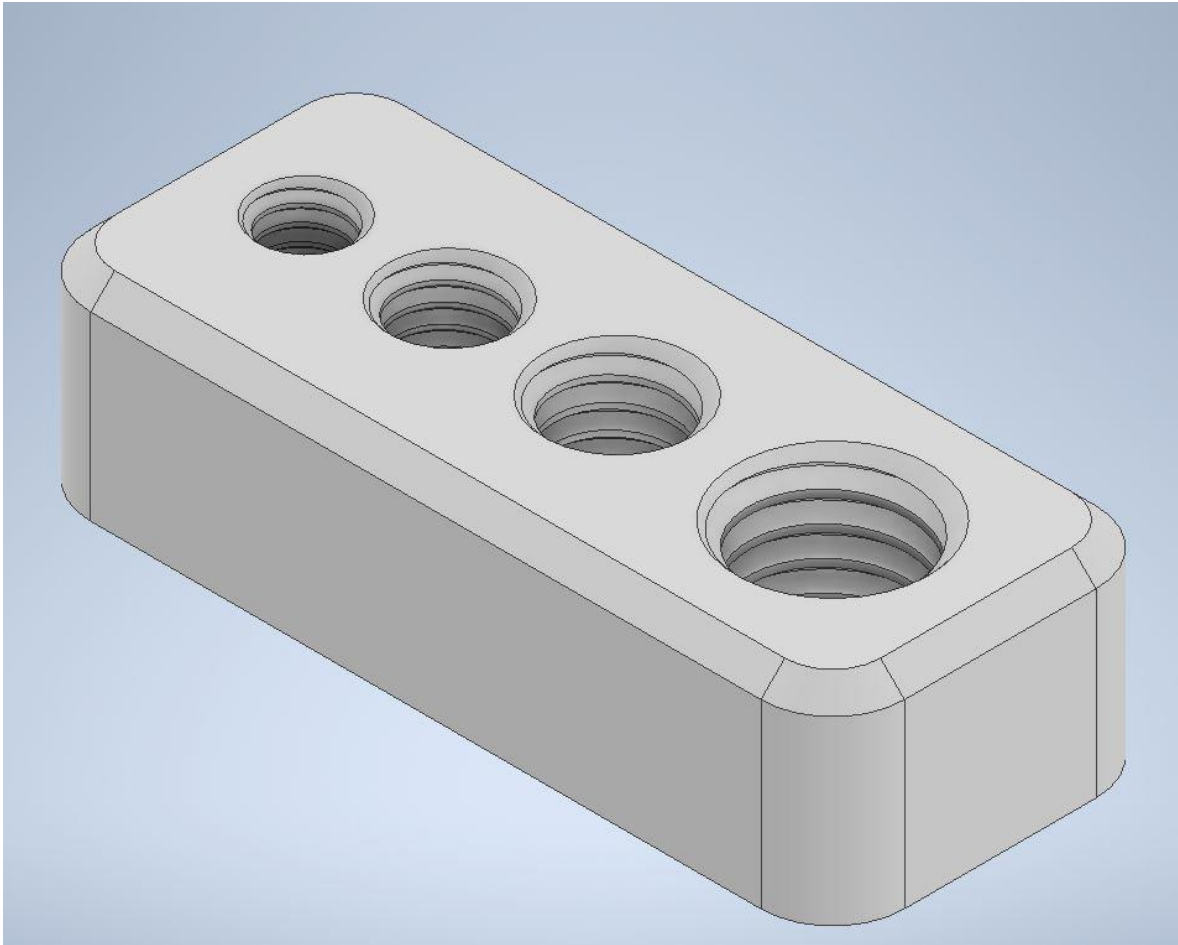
Probekörper mit M4 M5 M6 M8 Gewinde
